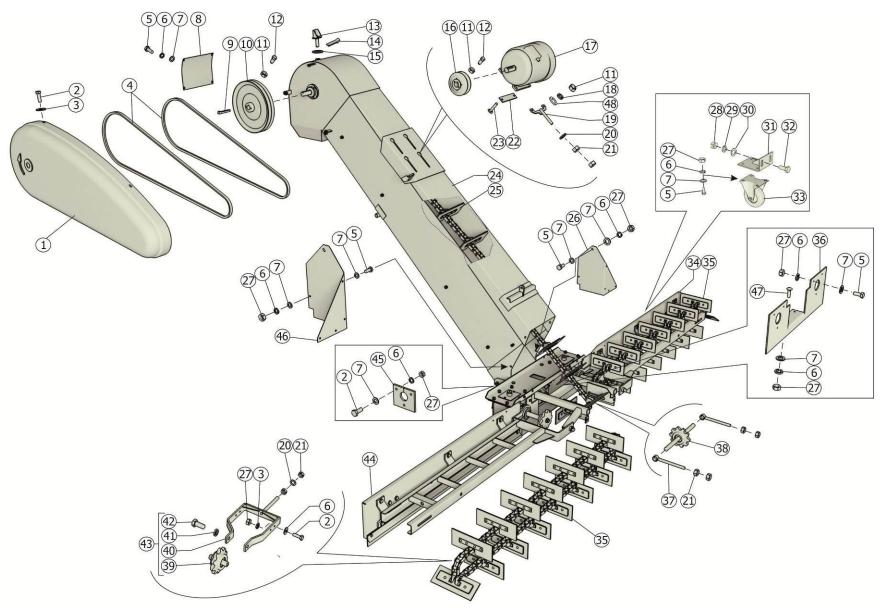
Транспортер загрузочный МЗС-90.03.000
